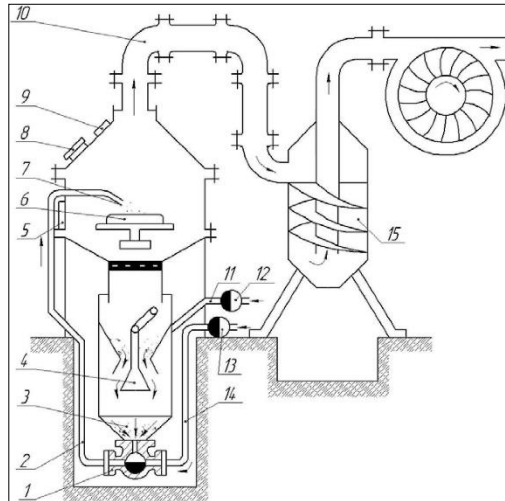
Установка для пневмомеханічного очищення деталей кісточковою крошкою:
